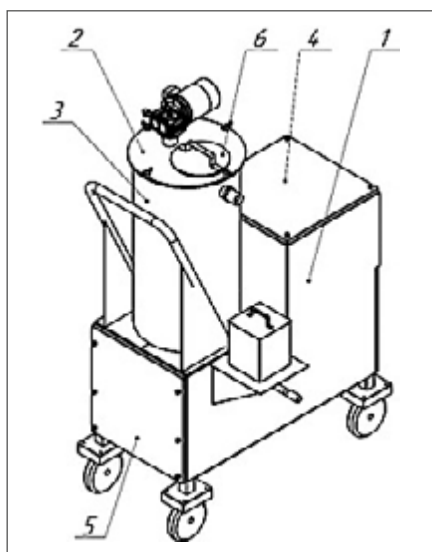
Аппарат для сбора пищевой крови: 1 – каркас; 2 – крышка резервуара; 3 – резервуар; 4 – крышка; 5 – крышка боковая; 6 – перемешивающее устройство
